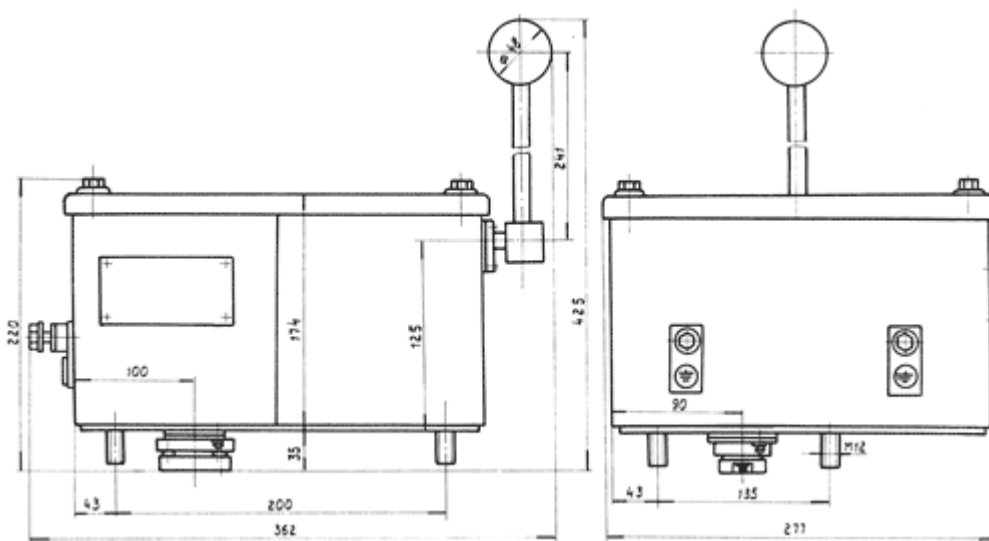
Габаритные и присоединительные размеры КАПВ
